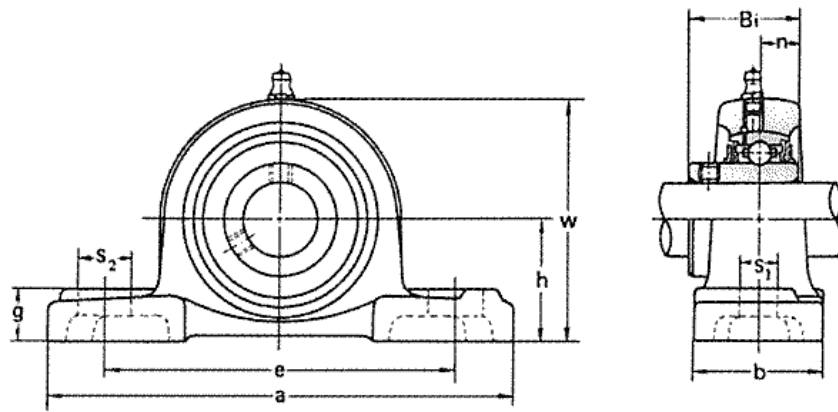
Розміри підшипника в корпусі UCP 210
